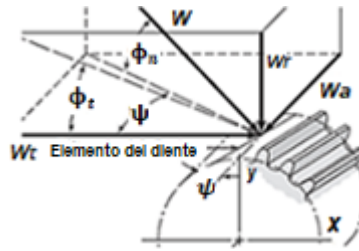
Fuerzas que actúan en un engranaje helicoidal.
